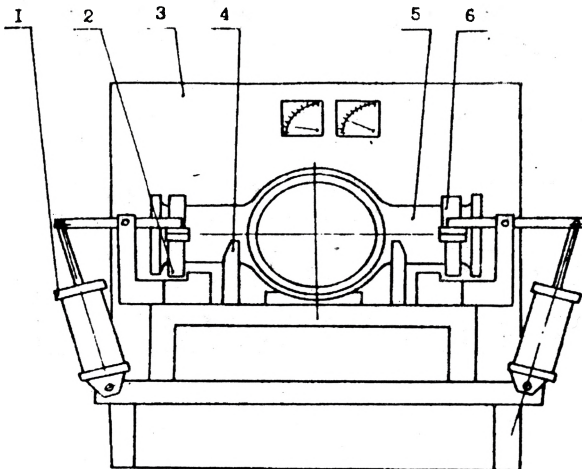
Установка для термообработки сварных кольцевых швов штамповарного картера заднего моста автомобилей МАЗ: 1 — нагревательный блок, 2 — обрабатываемый картер, 3 — нижняя часть индуктора, 4 — верхняя часть индуктора, 5 — призма для установки детали в индуктор, 6 — пневмоцилиндр прижима верхней части индуктора
